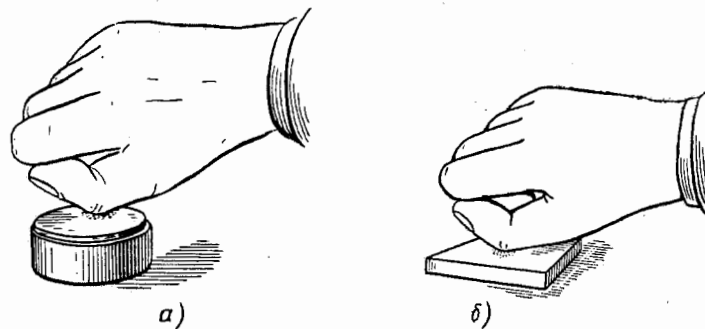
Полировальный инструмент, изготовленный из железа или мягкой стали.
